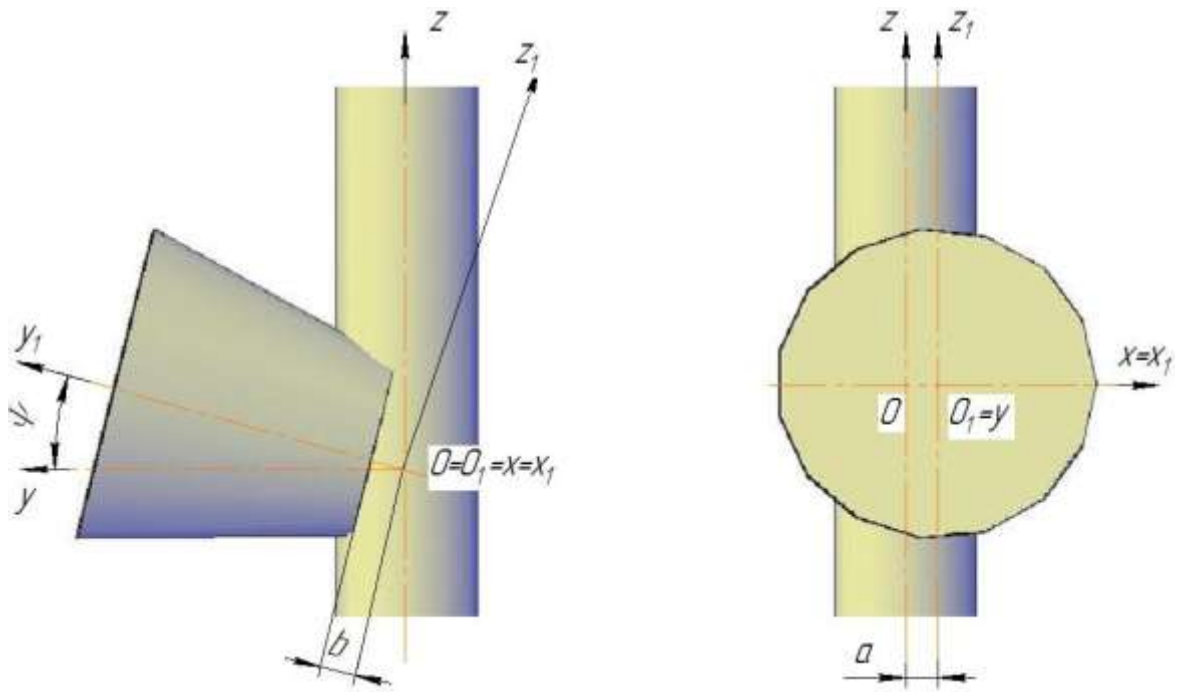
Системы координат, связанные с цилиндрической заготовкой и угловой фрезой
